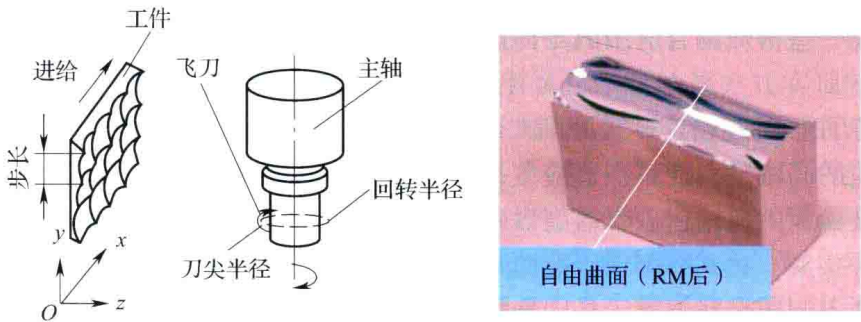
飞刀铣削加工原理及所加工后的自由曲面零件
